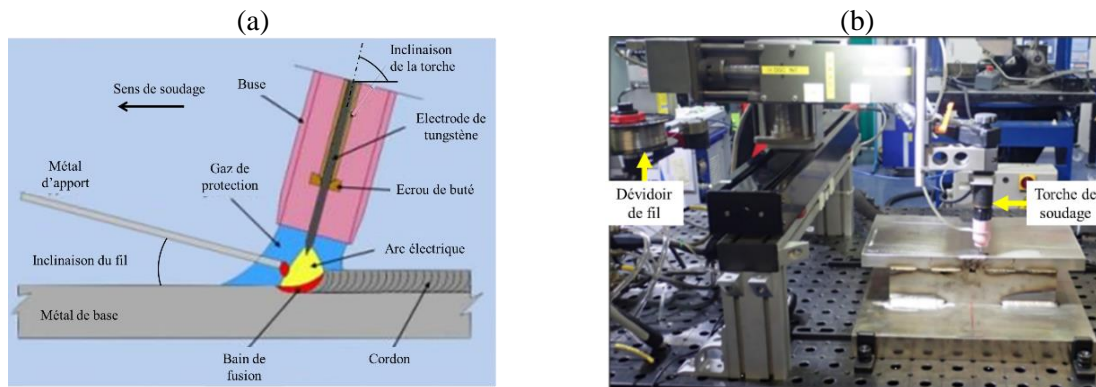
Principe du soudage TIG (a) (Foos 2017), et système de soudage robotisé du CEA utilisé dans le cadre de la thèse (b).
